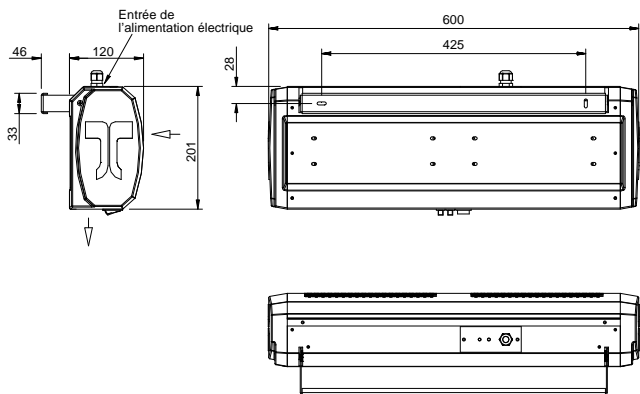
dessin d'assemblage général du rideau d'air JET 3+
